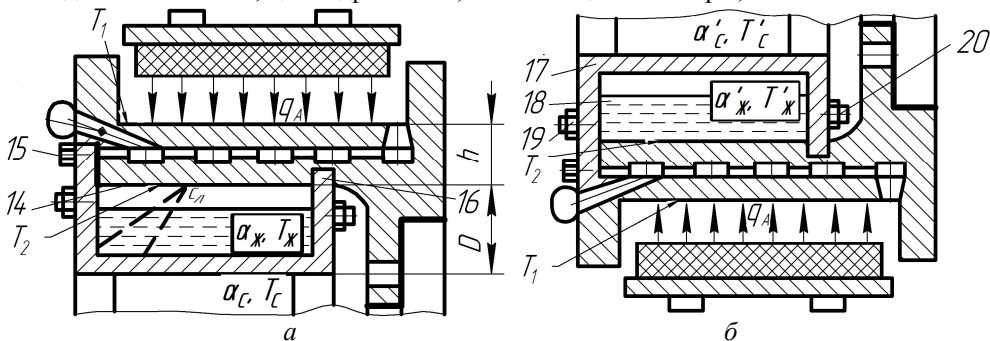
Воздушно-жидкостная система охлаждения пар трения ленточно-колодочного тормоза при положении сверху (а) и снизу (б) камеры с жидкостью: 14 – полированная нерабочая поверхность обода шкива; 15 – крепежный болт; 16 – продольный паз в обode шкива; 17 – камера шкива; 18 – жидкость; 19, 20 – клапаны: впускной; выпускной
